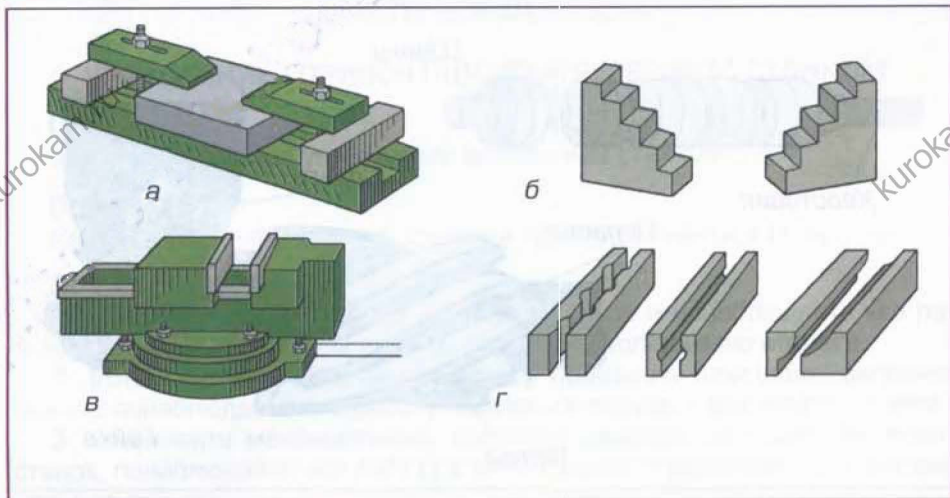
Механизмы и приспособления для закрепления заготовок на столе фрезерного станка: *а* – механизм крепления прихватами, *б* – ступенчатые подставки, *в* – машинные поворотные тиски, *г* – съёмные губки для тисков
